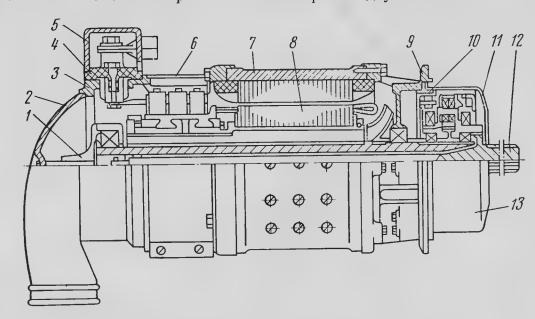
Разрез стартер-генератора СТГ-18ТМ 1с и 2с: 1— фланец; 2— патрубок; 3— коллекторный щит; 4— клеммная панель; 5— крышка; 6— защитная лента; 7— корпус; 8— якорь; 9— передний щит; 10— храповое колесо; 11— кожух; 12— приводной гибкий вал; 13— редуктор
